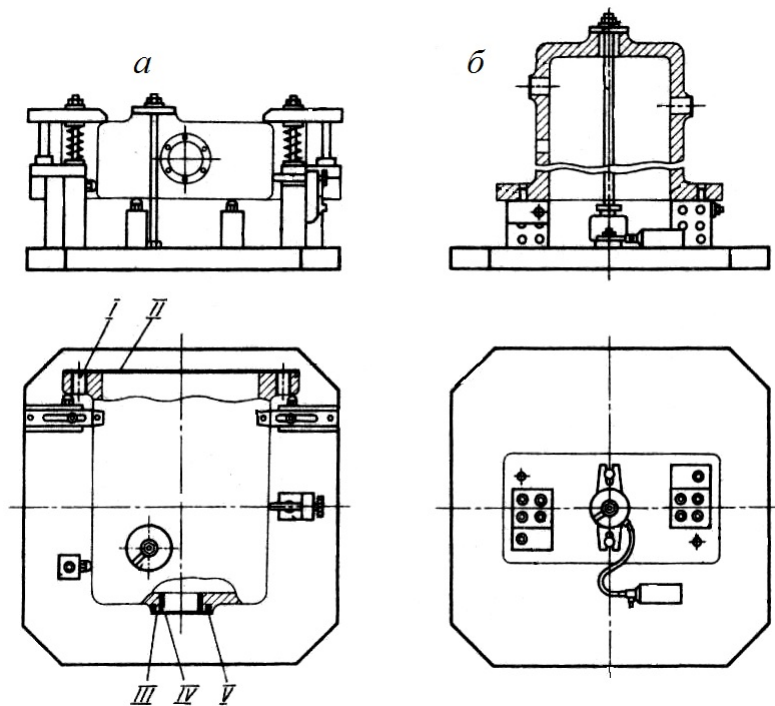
Компоновка приспособлений для обработки корпуса за два установка:
